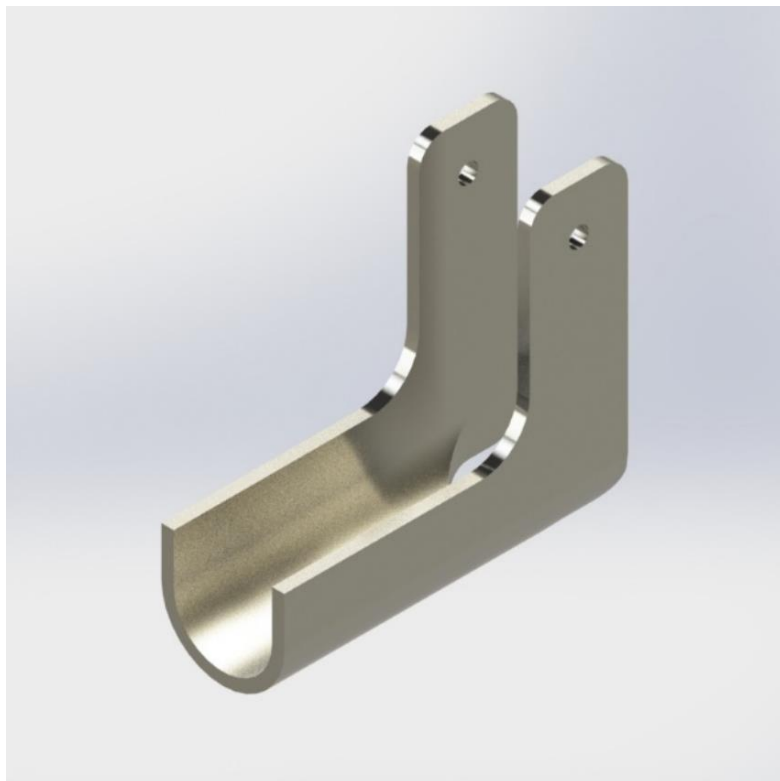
Peça obtida a partir do molde para dobrar chapa.
